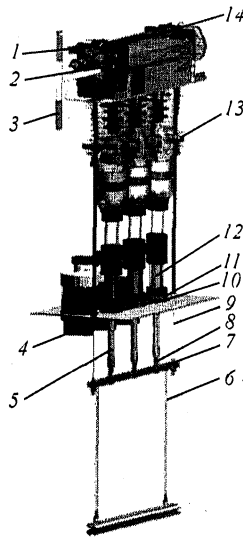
Разъединитель: 1 — фиксатор; 2 — вал разъединителя с системой тросов; 3 — рукоятка управления (съемная); 4 — кабельный приемник; 5 — тяговый изолятор; 6 — отключающая пружина; 7 — швеллер; 8 — пружина дополнительного контактного поджатия; 9 — трос; 10 — шина заземления (для разъединителя-заземлителя); 11 — гнездо заземления (для разъединителя-заземлителя); 12 — подвижный контакт разъединителя (разъединителя-заземлителя); 13 — элемент сборных шин модуля; 14 — вал фиксатора
